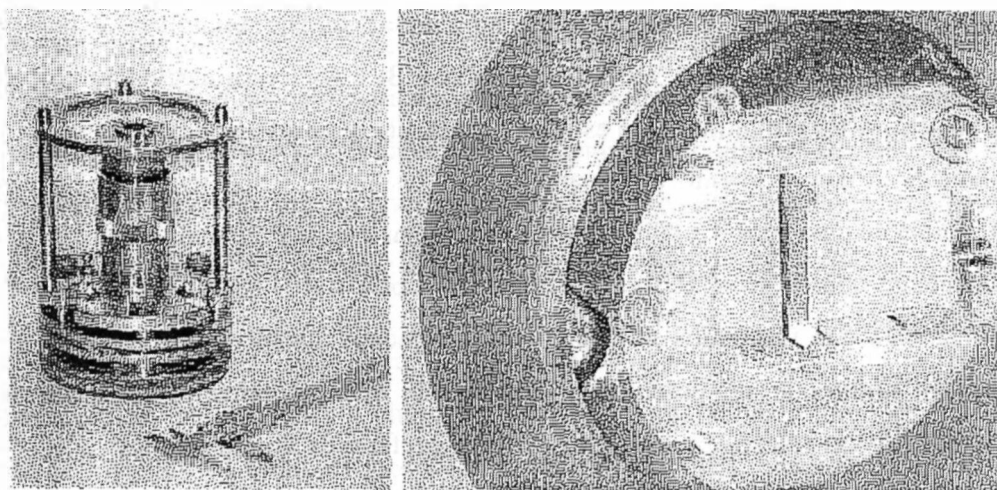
Jig utilizado para fixação de amostra durante o desbaste, à esquerda; fixação de amostra, à direita.
